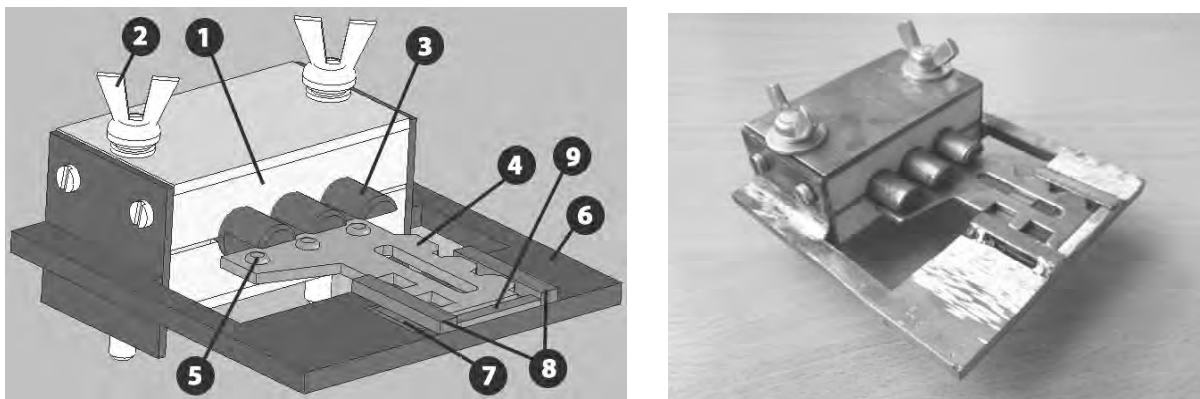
Приспособление для сборки-сварки засова: 1 – фторопластовый позиционер; 2 – шпилька; 3 – стержень засова; 4 – ригель засова; 5 – рельеф; 6 – основание приспособления; 7 – магнитный фиксатор; 8 – направляющие планки; 9 – упорная планка
